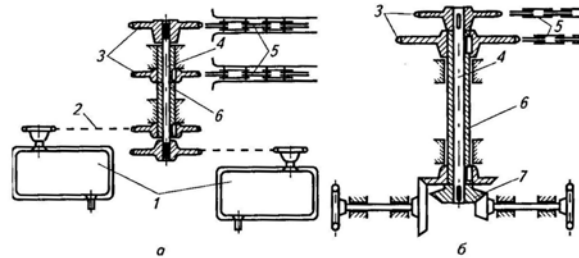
Схема приводів візкових конвеєрів: *a* – багатолінійного, *б* – двоярусного; 1 – редуктори; 2 – ланцюгові передачі; 3 – привідні зірочки; 4 – суцільний приводний вал; 5 – тягові ланцюги; 6 – полий приводний вал; 7 – кінчні зубчасті передачі
